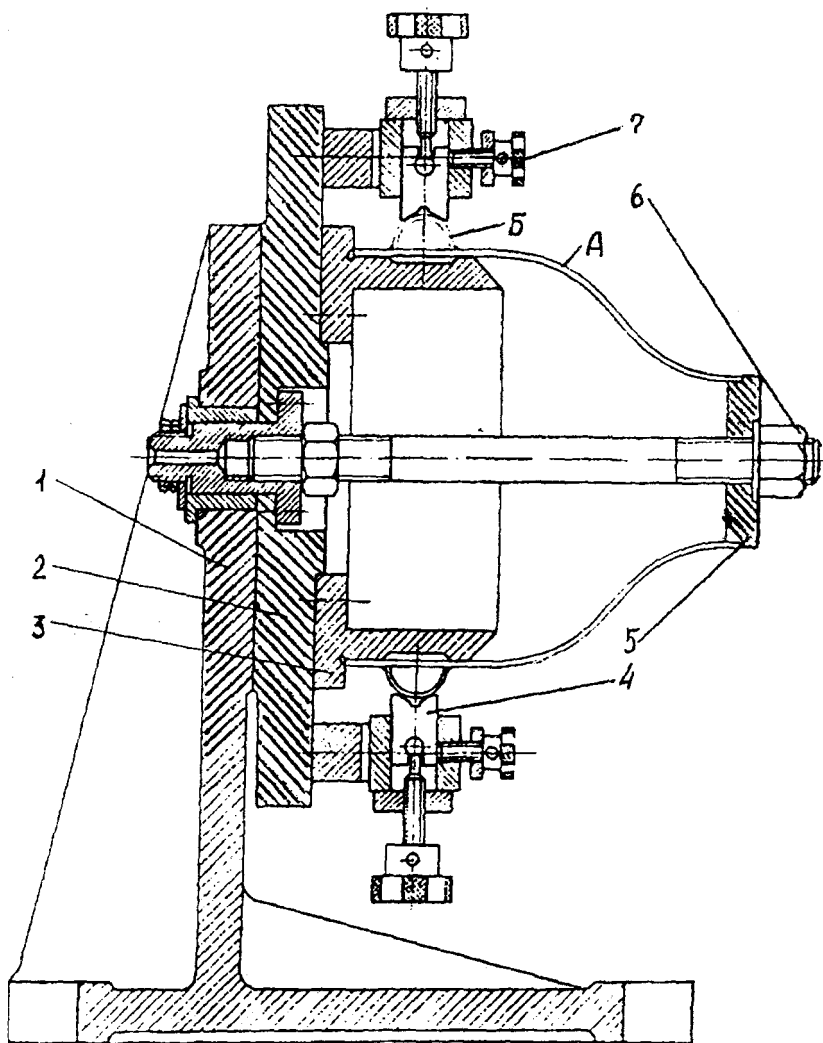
Приспособление-стапель для сборки и прихватки
